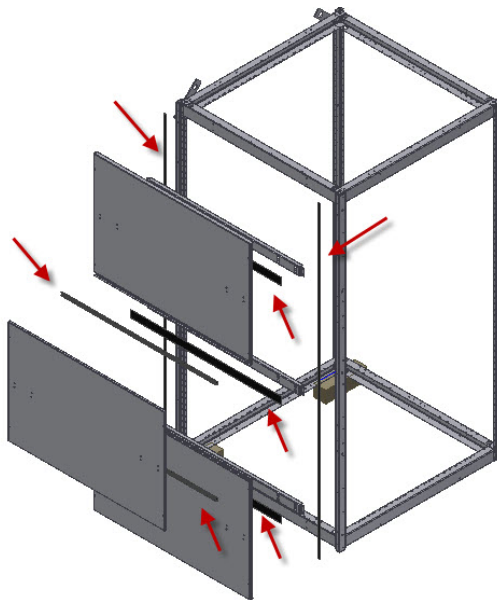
Explosivo de ensamble de cubiertas posteriores con posición de juntas para sellado.
